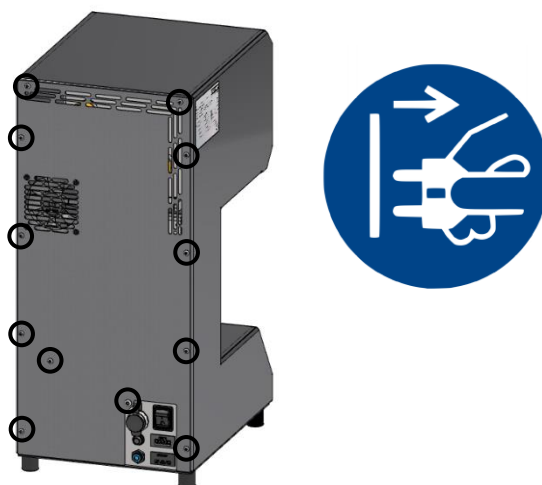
Pokrywa pieca (ilustracja poglądowa)
